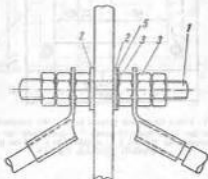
Fig. IV. Bolt de trecere pentru placa de pertinax (dimensiunile din paranteză sînt pentru bare de Ø6):
